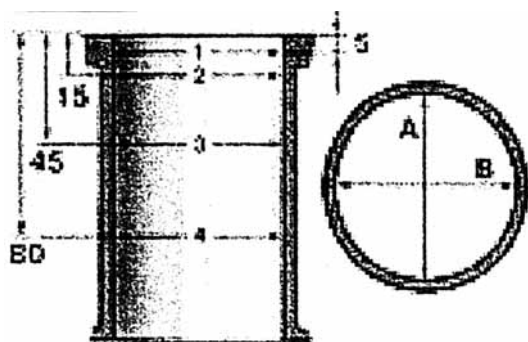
Контроль зеркала и блока цилиндров при их дефектации
